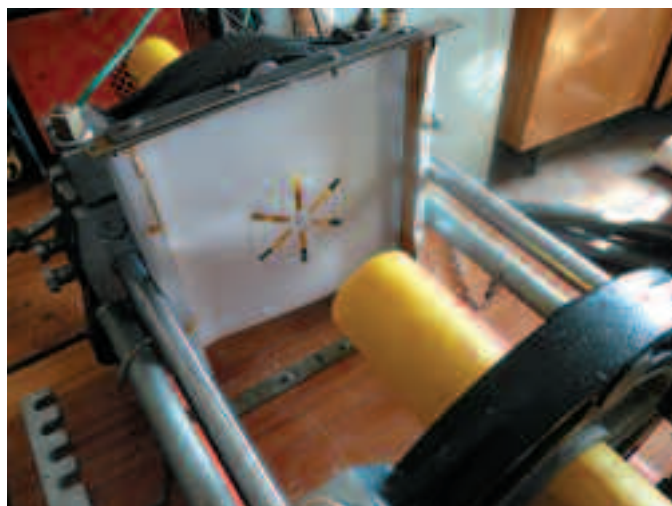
Установка шаблона для создания заданной площади сварки в сварном соединении
